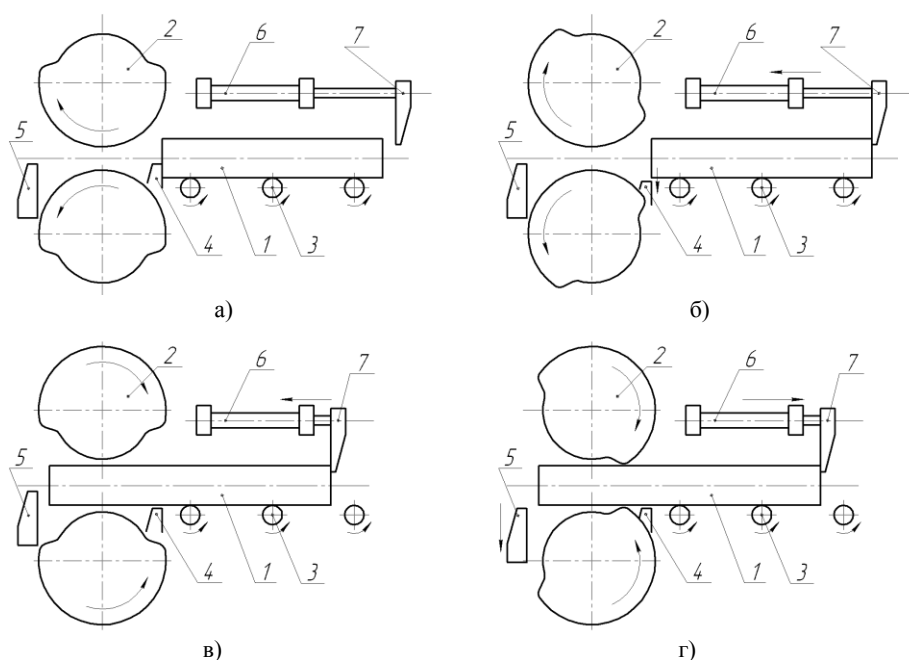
Принципиальная схема установки для предварительной вальцовки с пневматической загрузкой (а, б, в, г – стадии работы):
